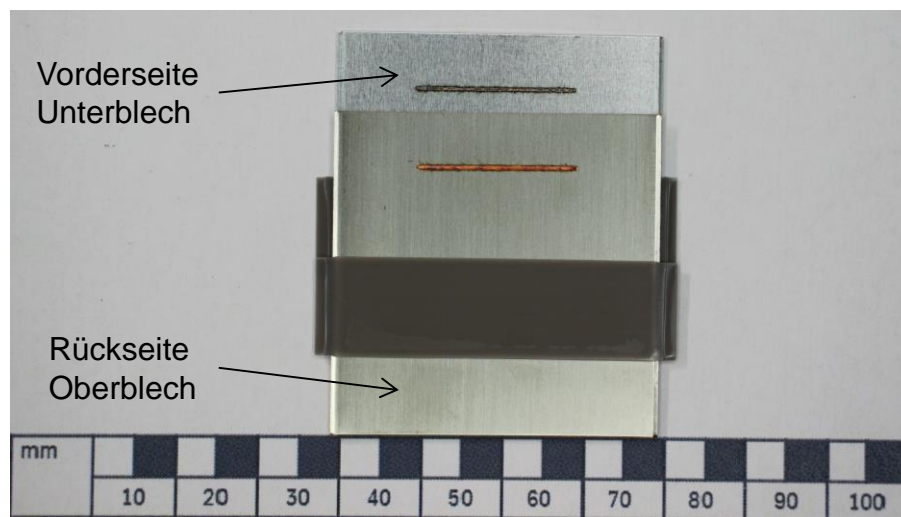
Fehlerhafte Verschweißung durch zu großen Schweißspalt
